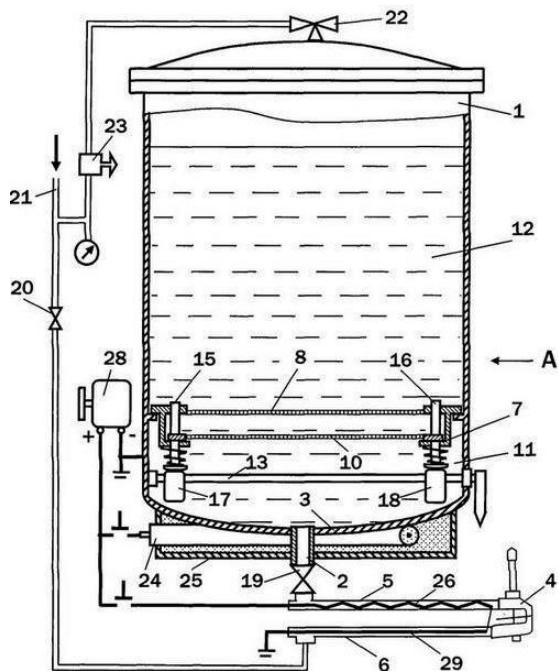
Устройство нагрева защитной смазки при нанесении по патенту № 2460590
